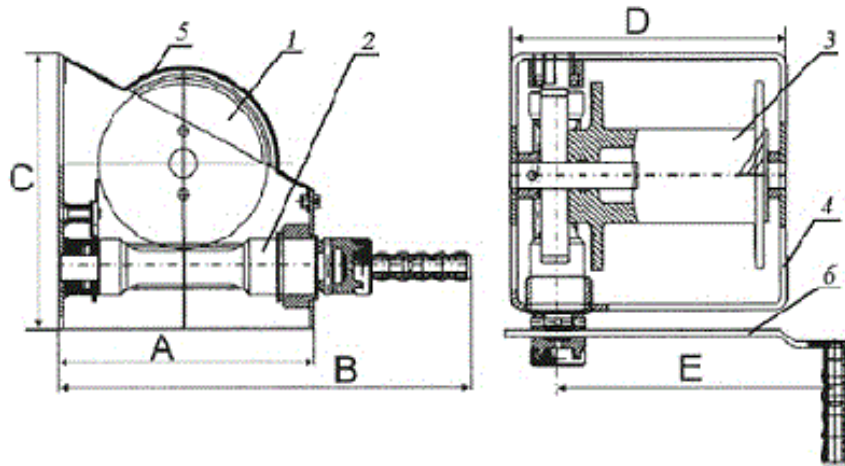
Схема Лебедки HW-AB 1000: 1-колесо; 2-червячный вал; 3-барабан; 4-корпус; 5-кожух; 6-рукоятка. Деталь – червяк, входит в редуктор и предназначен для передачи крутящего момента от рукояти на барабан.
